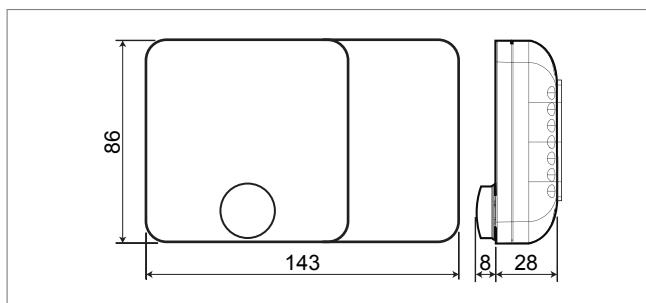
Dimenzijski crtež upravljačkog terminala zone za montažu na željenu površinu (dimenzije u mm)
